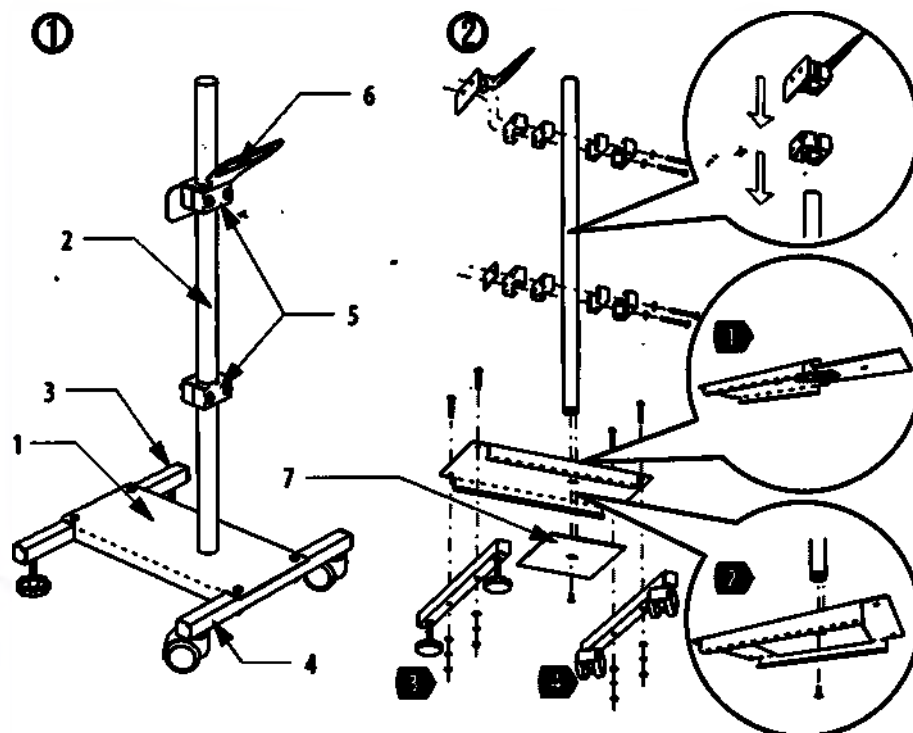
Общая конструкция и схема сборки передвижной подставки КШУР.301422.001.
